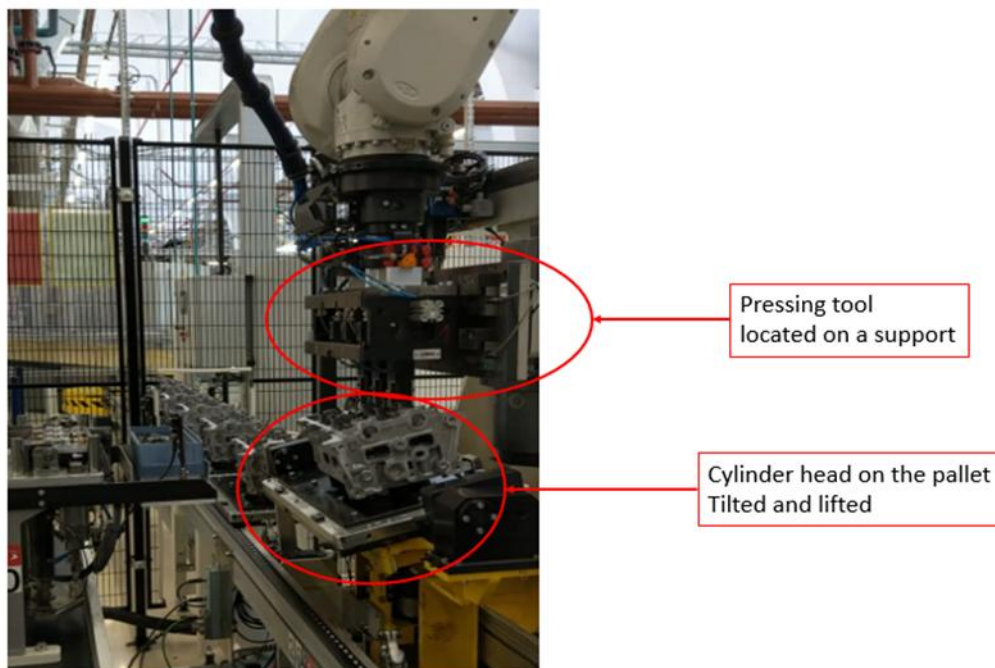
Станция по запрессовки тарелок + сухарей
